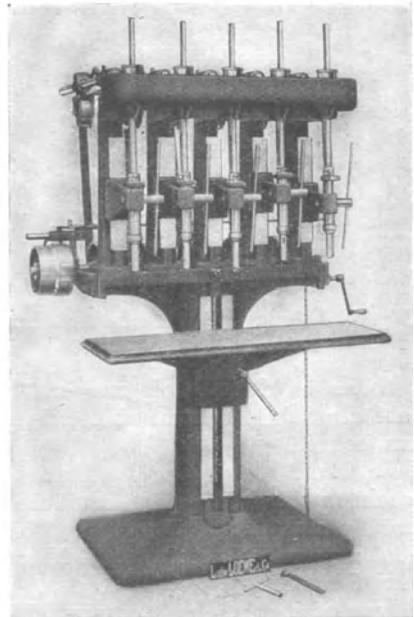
Mehrspindelige Senkrecht-Bohrmaschine.
